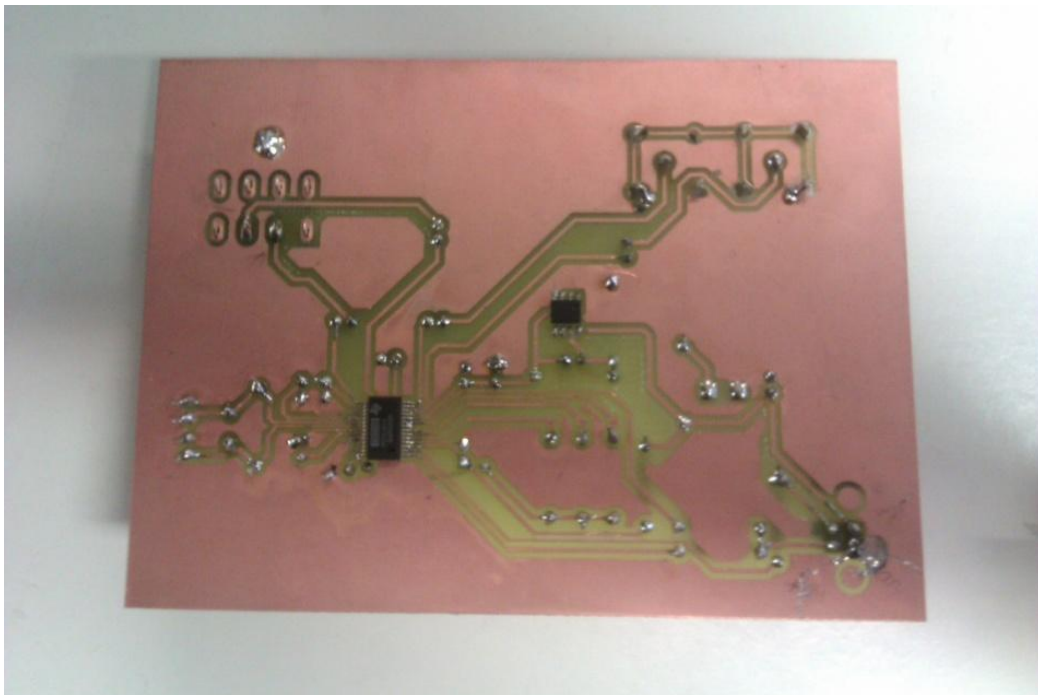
Tercer montaje realizado de la tarjeta de sonido sobre la PCB.
